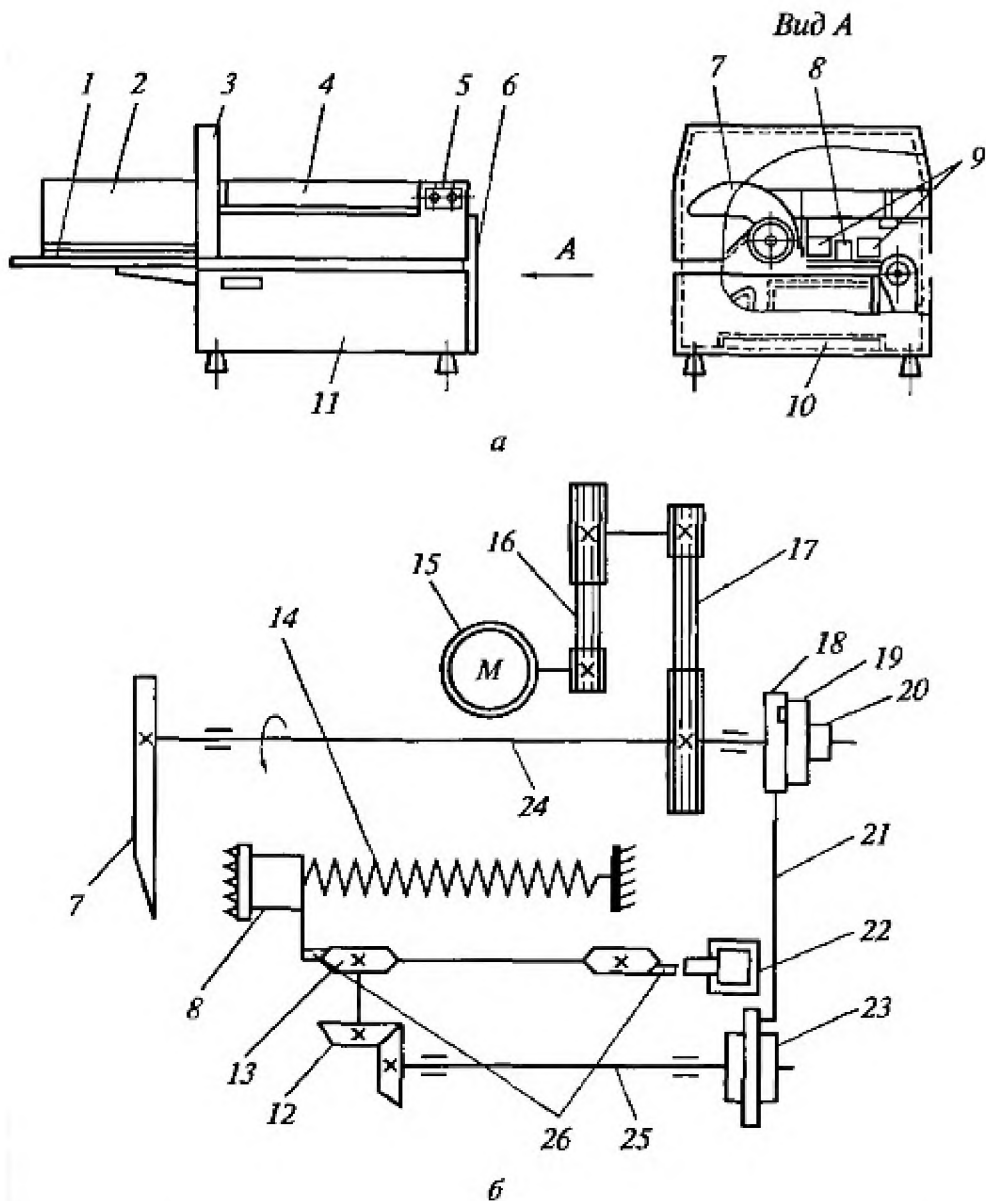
Хліборізка АХМ 300: а – вигляд загальний; б – схема кінематична; 1 – лотік розвантажувальний; 2, 4 – кришки; 3 – огороження ножа; 5 – вимикач двокнопочний; 6 – дверцята; 7 – ніж серпоподібний; 8 – виштовхувач; 9 – пластинки притискні; 10 – ящик для збирання крихти; 11 – корпус; 12 – передача конічна; 13 – подавач ланцюговий; 14 – пружина; 15 – електродвигун; 16, 17 – клинопасові передачі; 18 – ексцентрик; 19 – регулятор; 20 – гайка; 21 – шатун; 22 – кінцевий вимикач; 23 – муфта обгінна; 24 – вал головний привідний; 25 – вал; 26 – пальці
